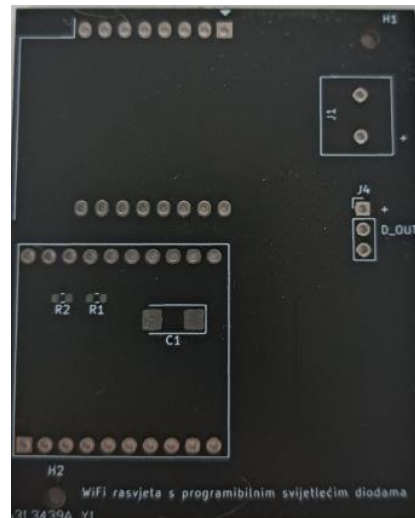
Dizajn PCB-a u KiCAD-u
